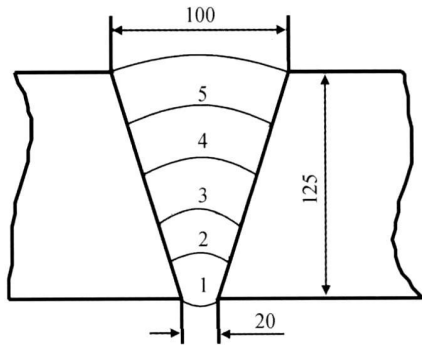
焊道数为 5 道时的焊接顺序及尺寸
